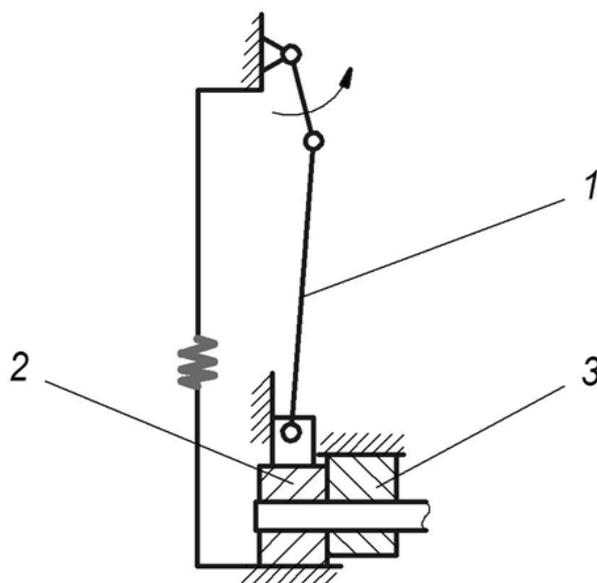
Отрезка заготовок прутка силами упругой реакции станины [7].
